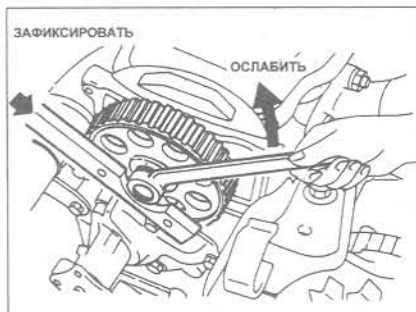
Блокировка зубчатого шкива распредвала (Глава 17)
